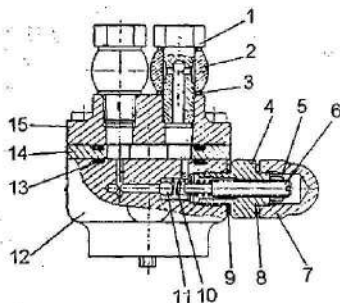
Редукционный клапан топливного насоса: 1 - болт топливпровода; 2 - угольник поворотный; 3, 8, 9, 13 - кольца уплотнительные; 4 - штуцер; 5, 7 - гайки; 6 - винт регулировочный; 10 - пружина; 11 - шарик; 12 - корпус топливного насоса; 14 - прокладка; 15 - крышка топливного насоса.
